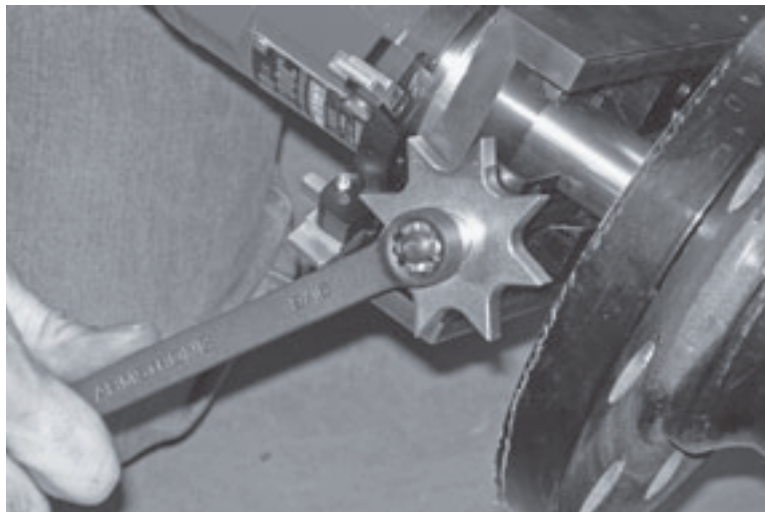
Drehen Sie das Sternrad nach links, um den Werkzeugschlitten bis hinter den Flanschaußendurchmesser zurückzufahren.
